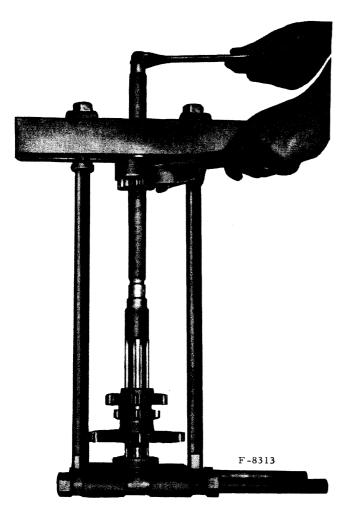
Montage du roulement arrière sur l'arbre intermédiaire.
